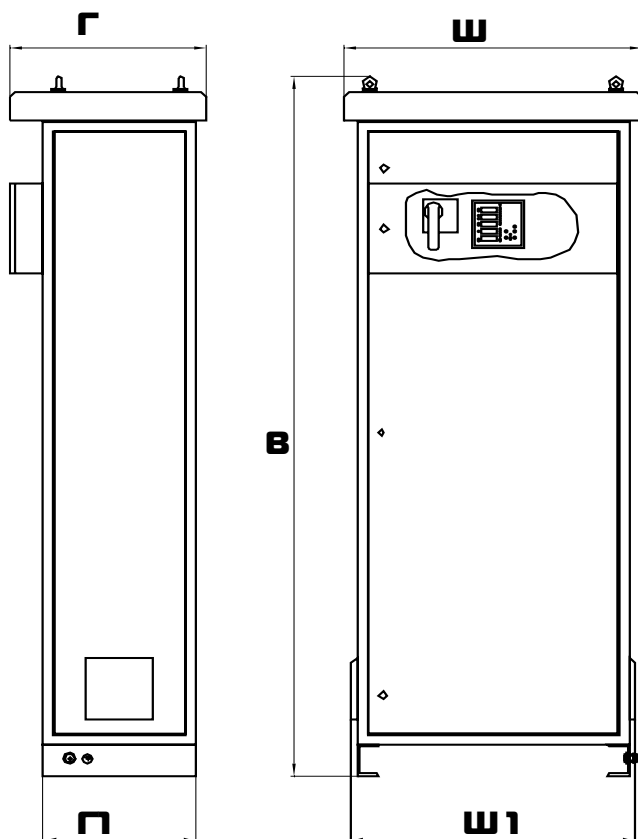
Габаритный чертеж трехфазного СДТ 10-100кВА IP20
